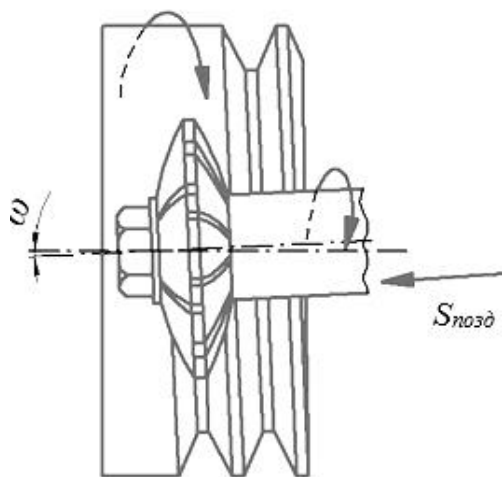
Схема нарізування різьби дисковою фрезою
